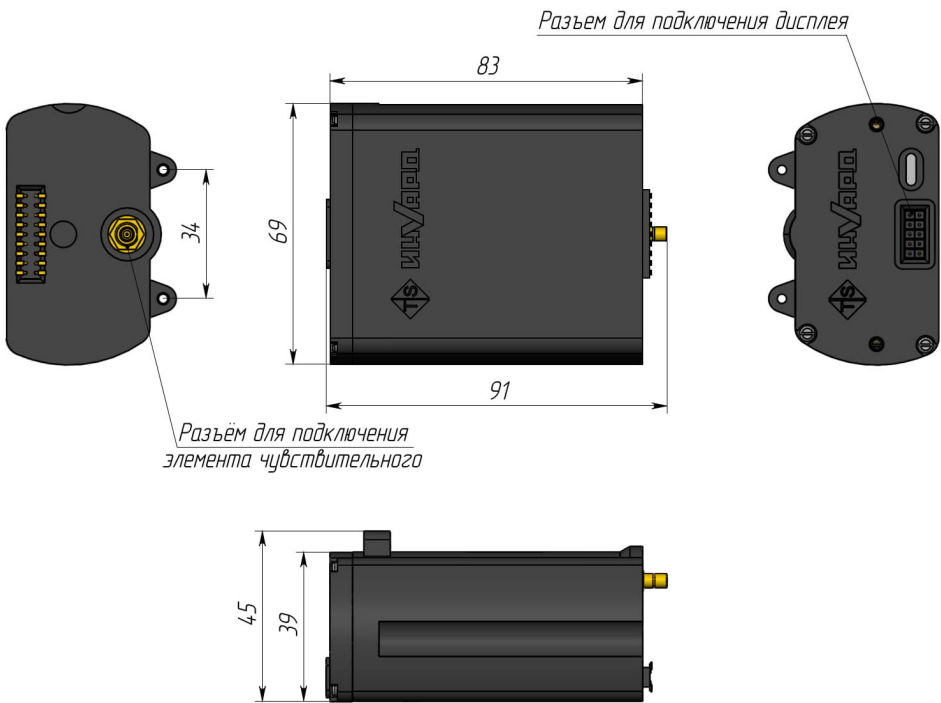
Габаритные и установочные размеры блока электронного ТЕКФЛЕКС для алюминиевого мини корпуса
